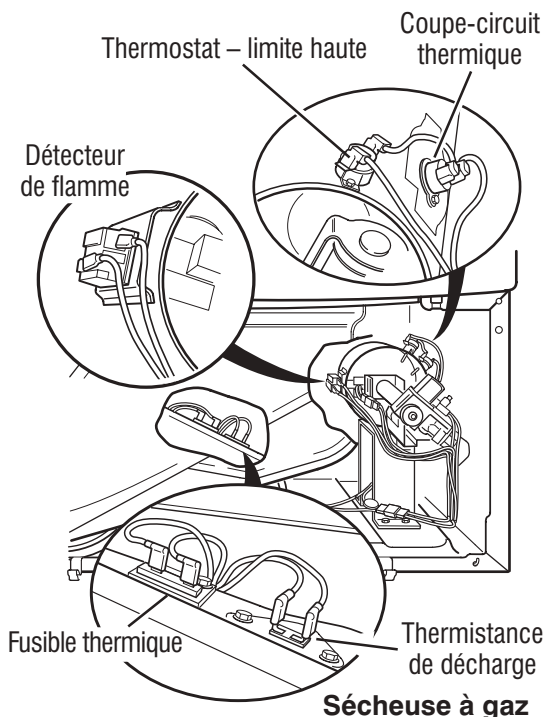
Composants thermiques, sècheuse à gaz, vue de face.
